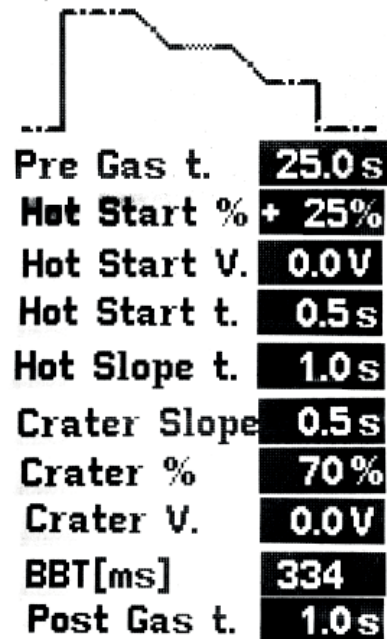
Pantalla de los ajustes en Root Welding
